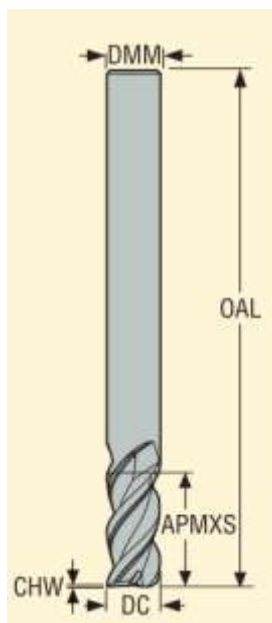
Фреза для фрезерования шпоночного паза на валу К-12-
